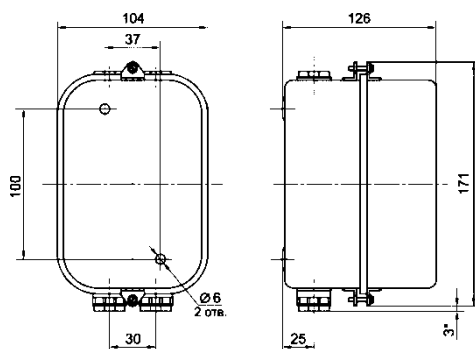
Пускатель ПМ12-010 10А в защитном корпусе - IP40; IP54.
